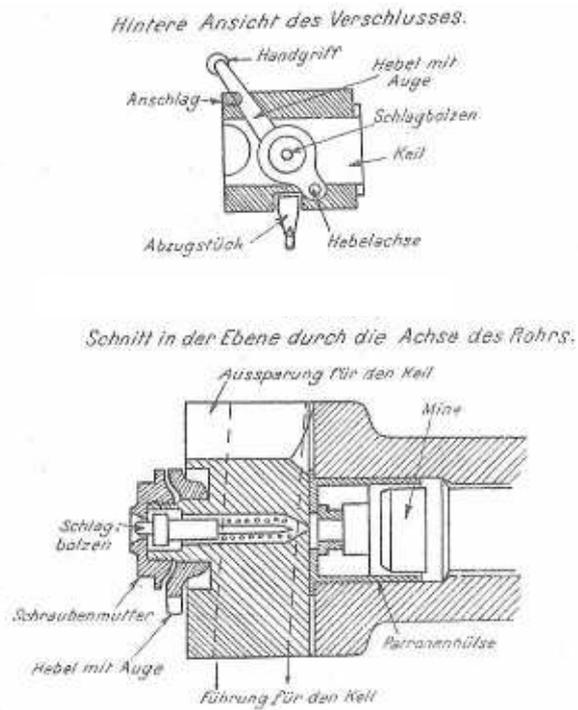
Verschlussaufbau des 75 mm mortier T,
